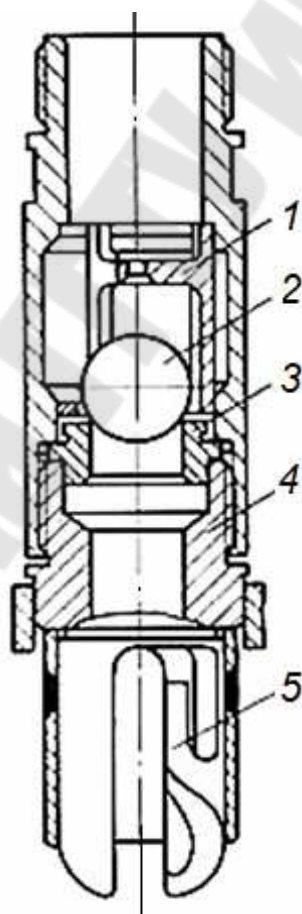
Нижний нагнетательный клапан насосов НГН-2 с ловителем для захвата штока всасывающего клапана: 1 – клетка клапана; 2 – шарик; 3 – седло клапана;
